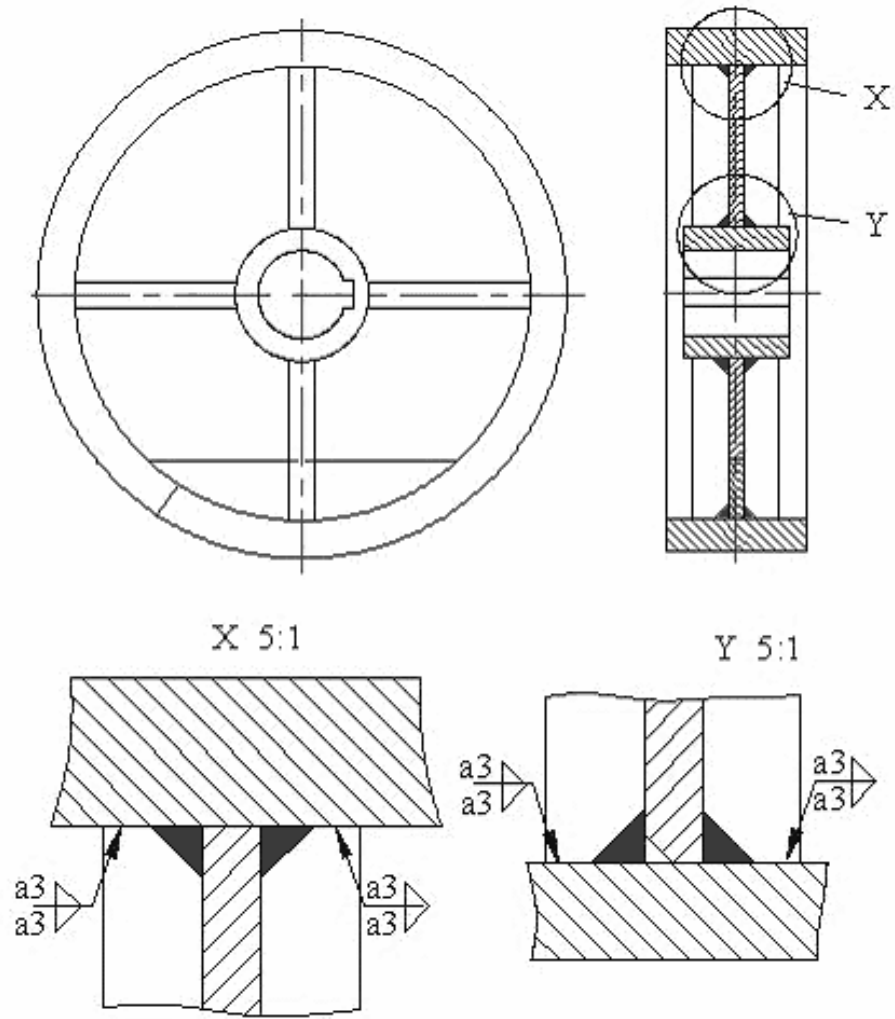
Çepeçevre köşe kaynağın belirtilmesi
